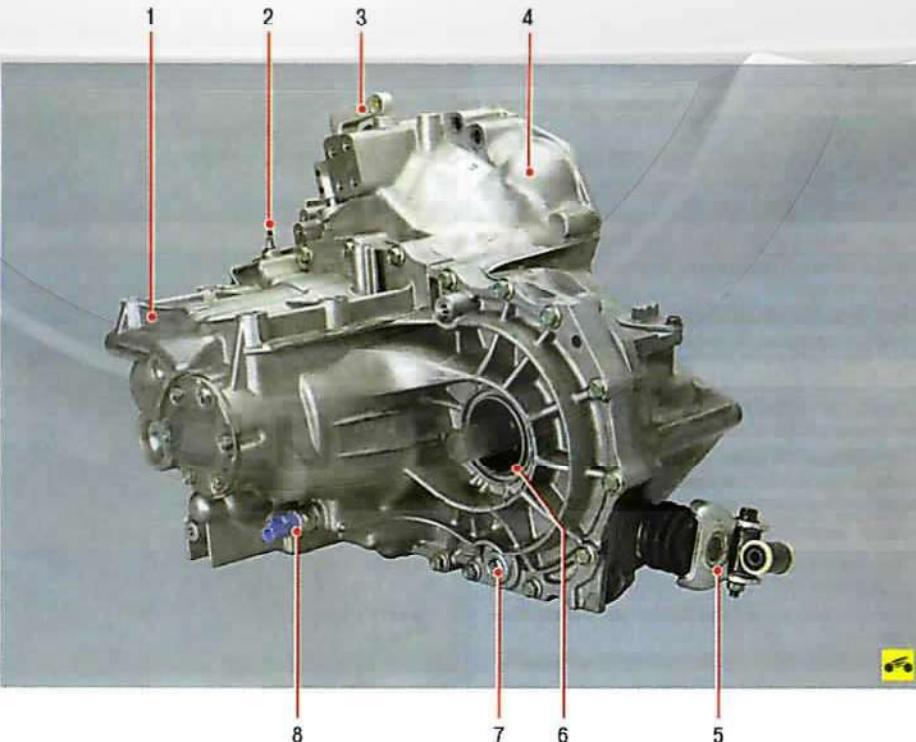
Механическая коробка передач: 1 – картер коробки передач; 2 – сапун; 3 – рычаг вилки выключения сцепления; 4 – картер сцепления; 5 – механизм выбора передач; 6 – сальник полусоси; 7 – пробка отверстия для слива масла; 8 – датчик нейтрального положения передач
